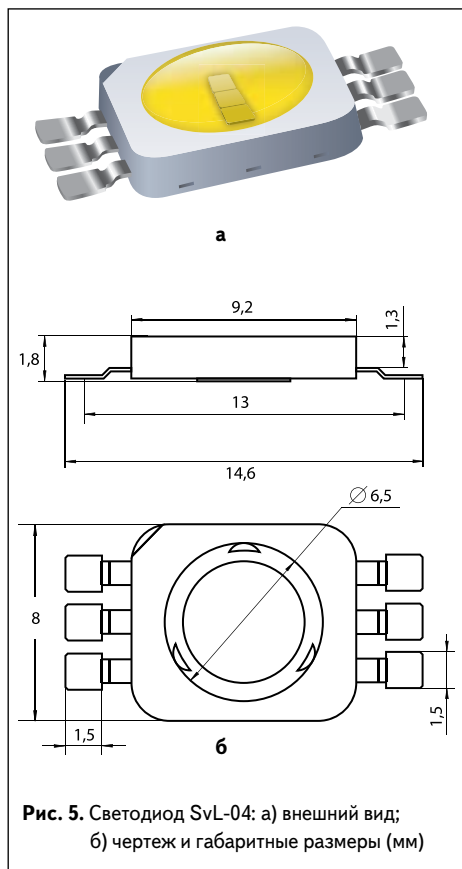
Светодиод SvL-04: а) внешний вид; б) чертеж и габаритные размеры (мм)
